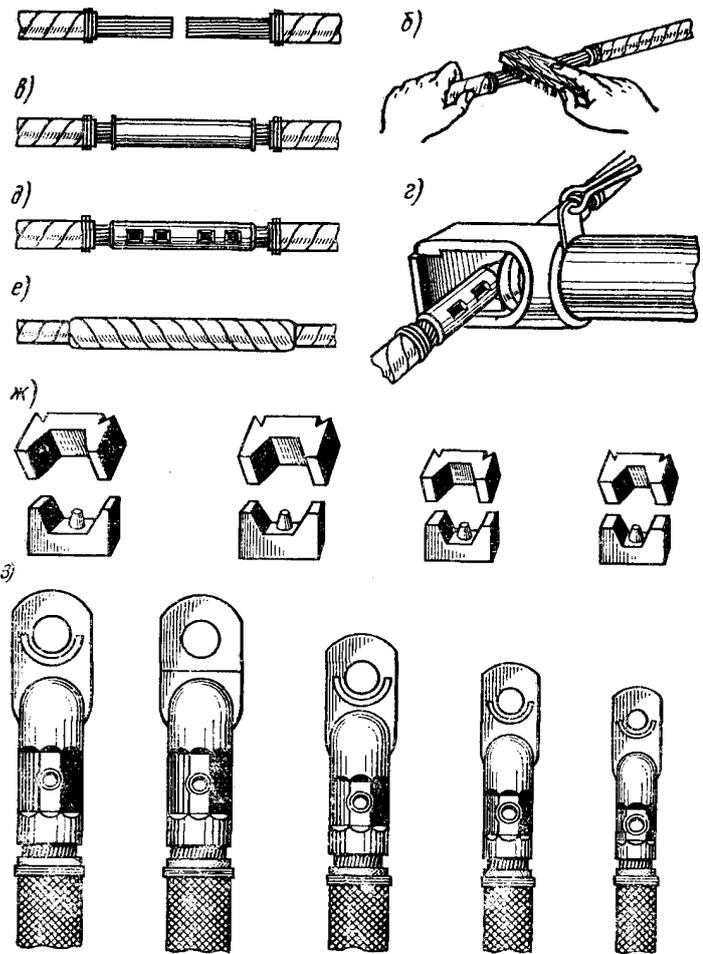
Технология опрессовки при соединении алюминиевых жил сечением 16...240 мм²: а - концы жил со снятой изоляцией; б - зачистка жил; в - подготовленное соединение; г - опрессовка; д - опрессованное соединение; е - готовое изолированное соединение; ж - набор матриц к пуансонов; з - напрессованные наконечники
